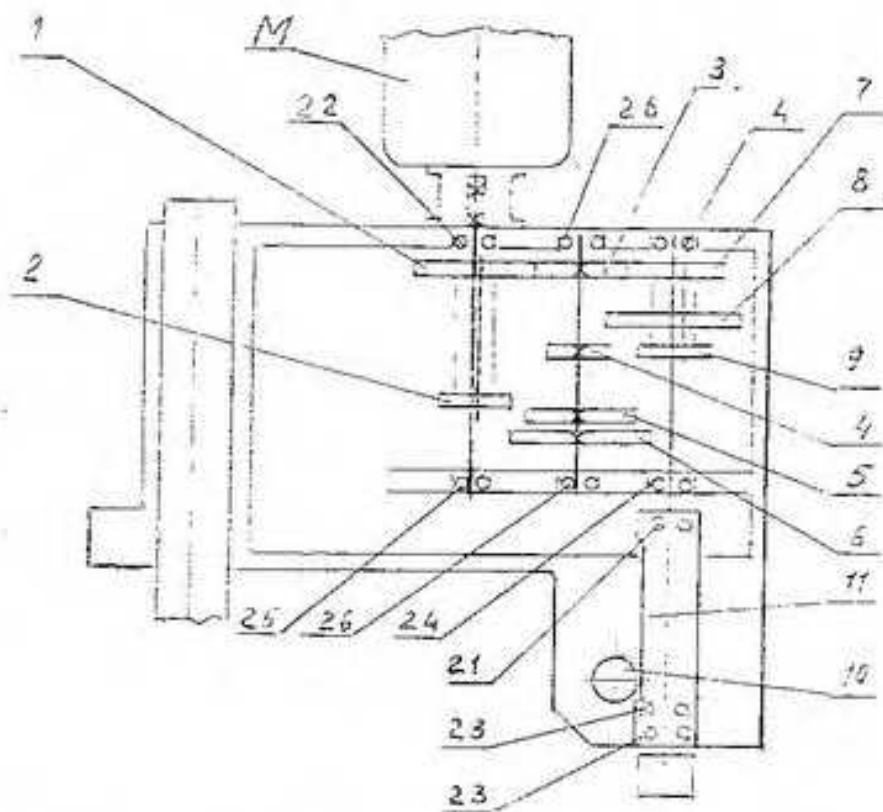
Кинематическая схема сверлильной головки и схема расположения подшипников
